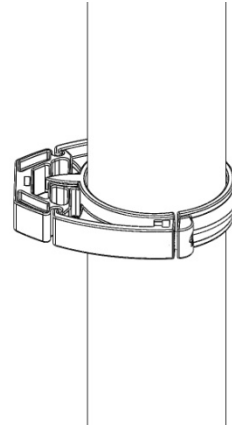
b : Phonoklip coulissant en position haute (avec entretoise) et serrant en position basse (entretoise retirée)
